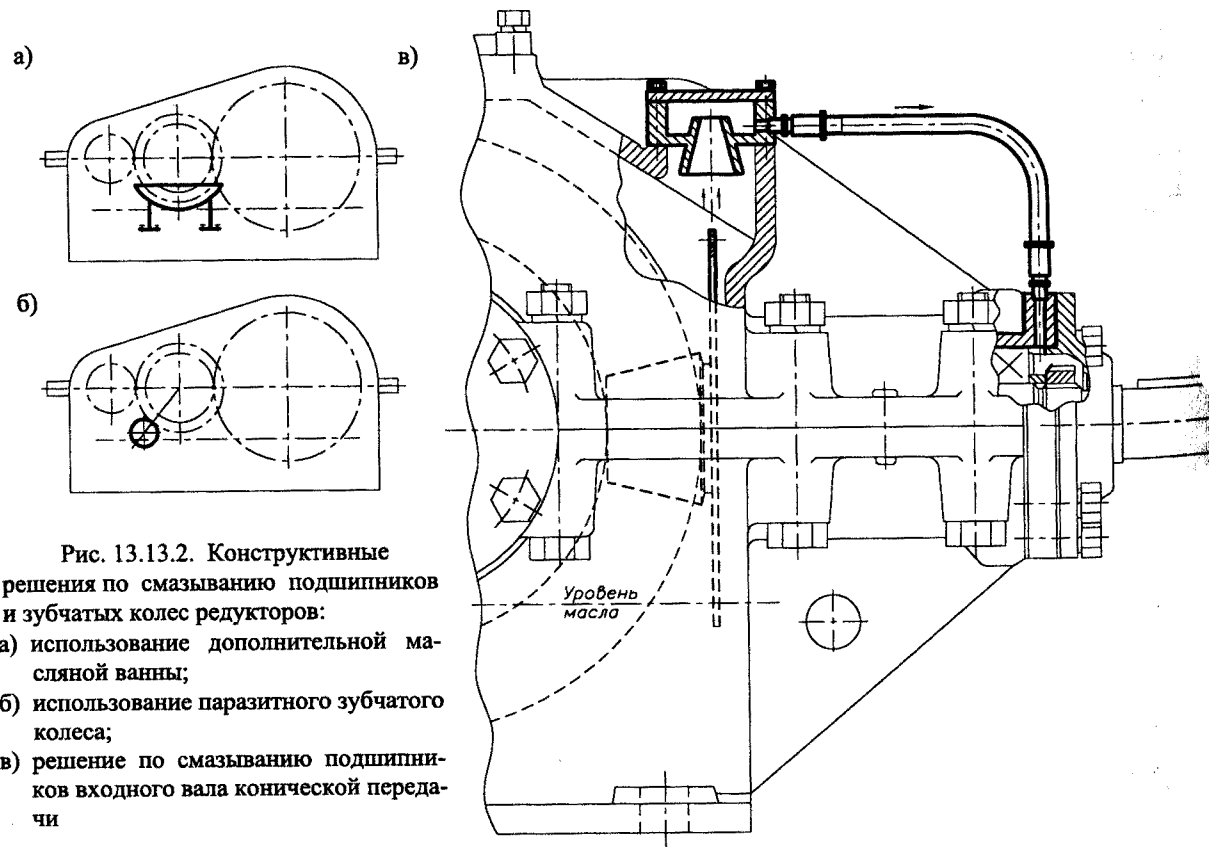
Конструктивные решения по смазыванию подшипников и зубчатых колес редукторов:
